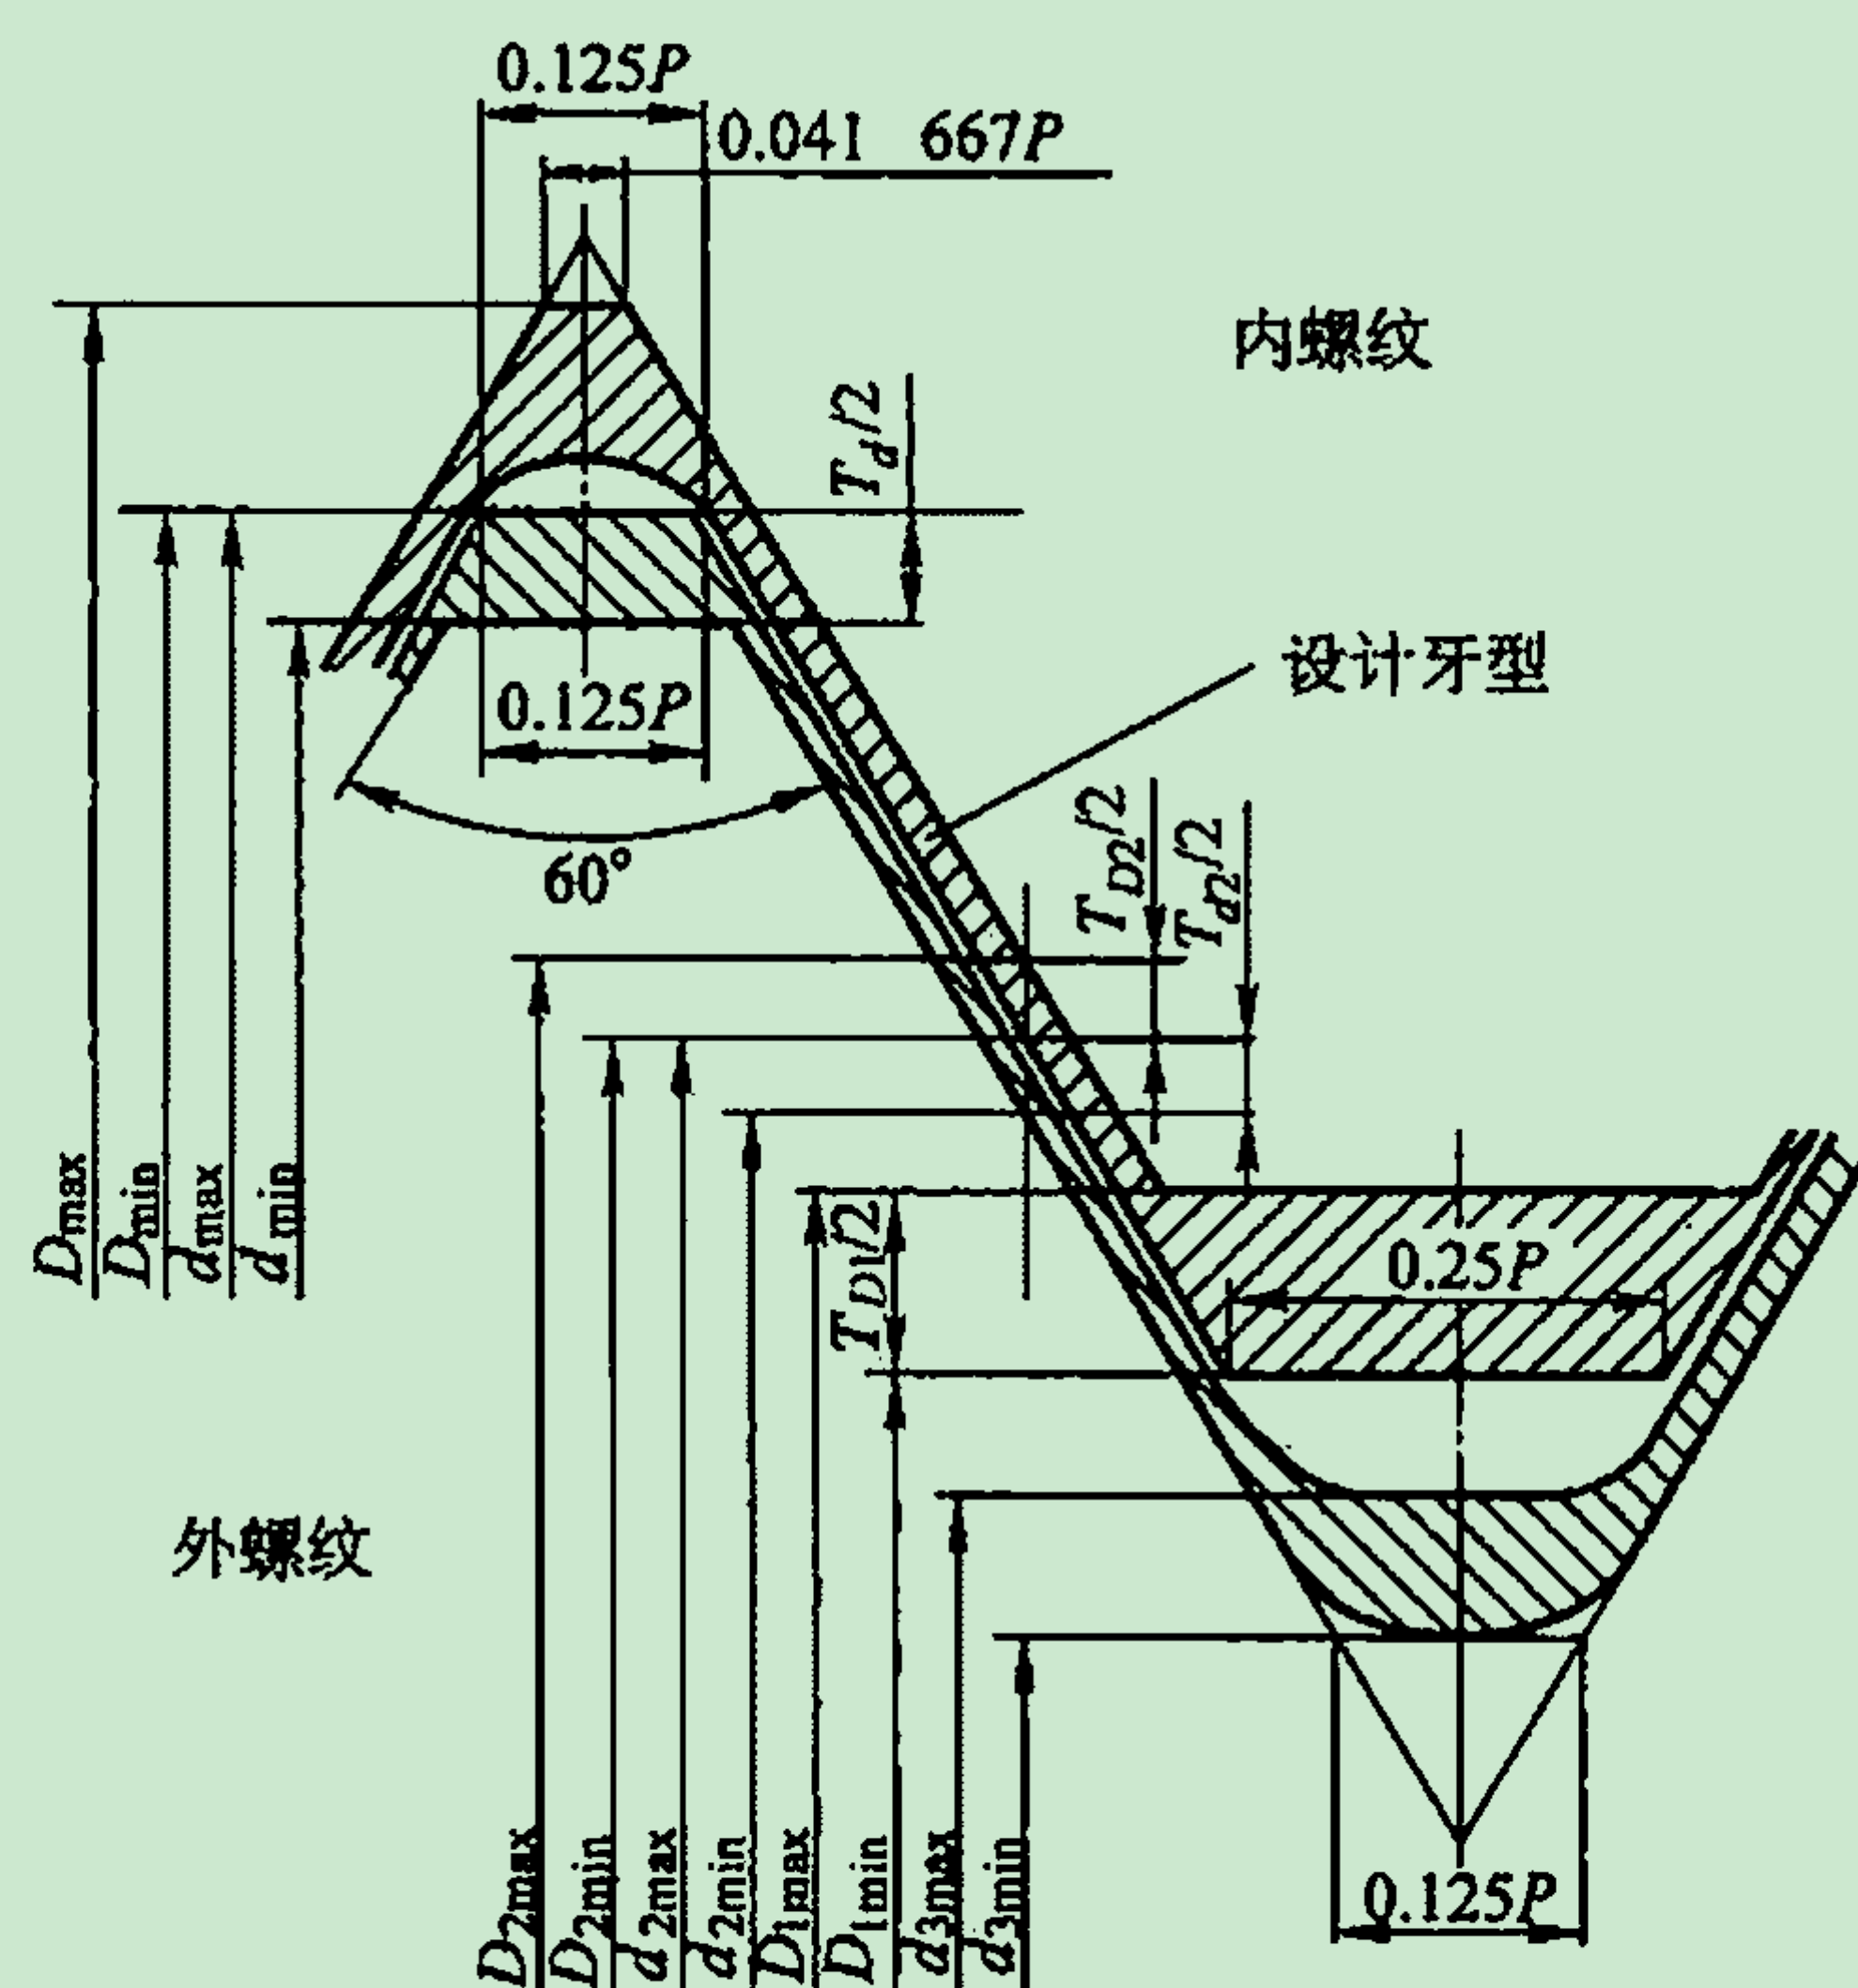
1A、2A、1B 和 2B 螺纹的公差带位置
